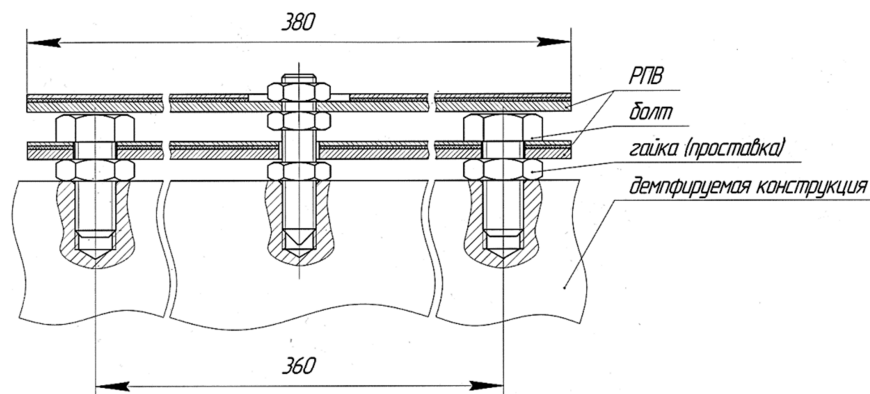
Схема установки РПВ с одноопорным креплением над РПВ с двухопорным креплением
